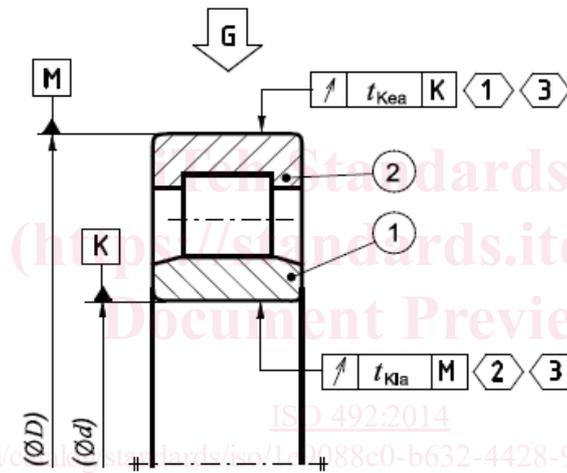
Геометрические допуски отдельных деталей подшипника с цилиндрическим отверстием
